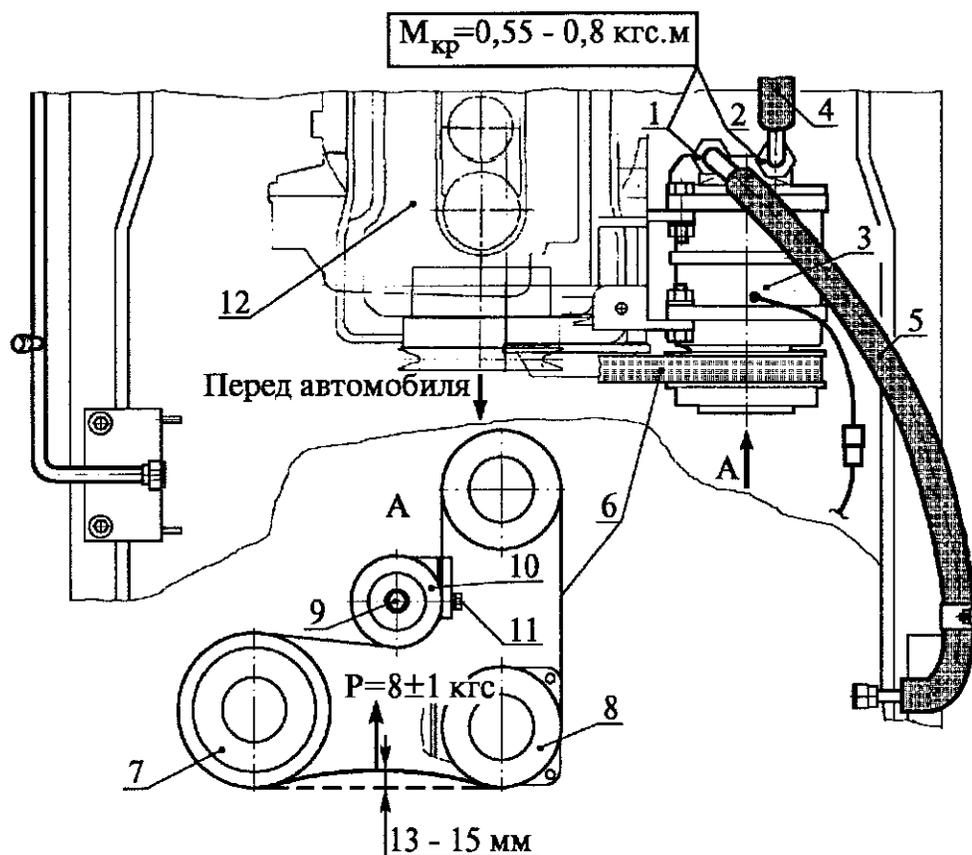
Подсоединение шлангов к компрессору и натяжение ремня привода компрессора:
